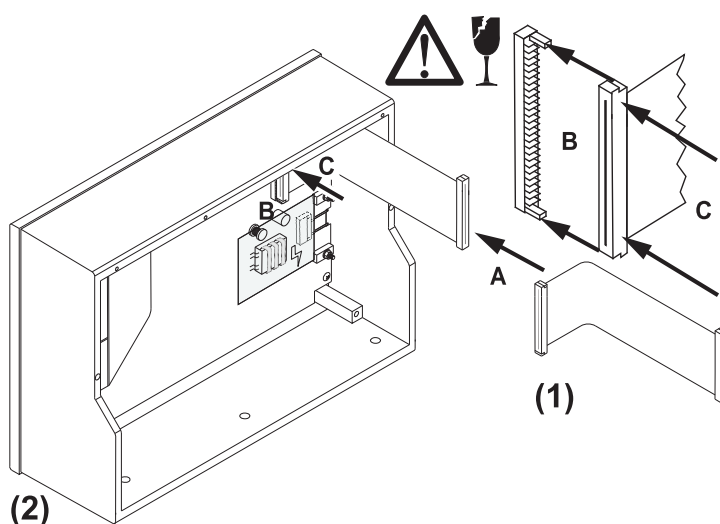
Aufstecken des Flachband-Anschlusskabels auf die Displayplatine
